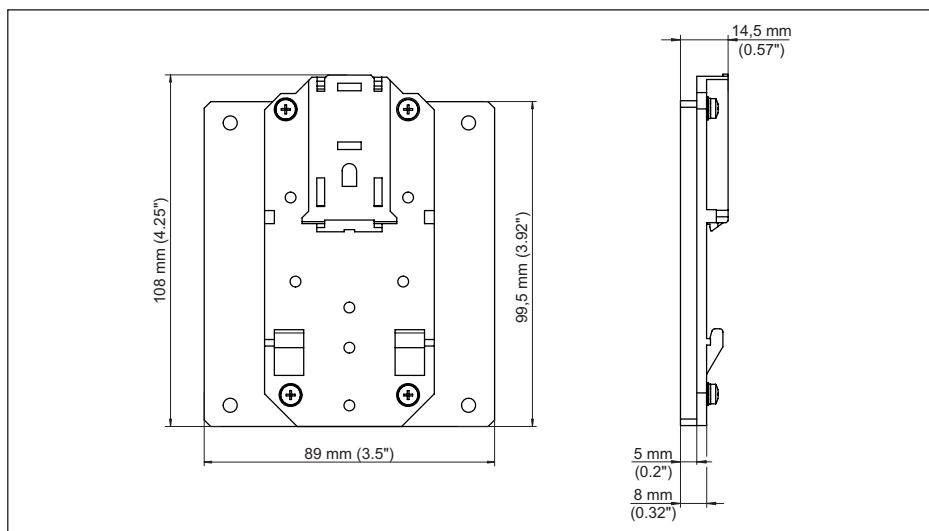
Размеры дополнительного адаптера для несущей рейки
